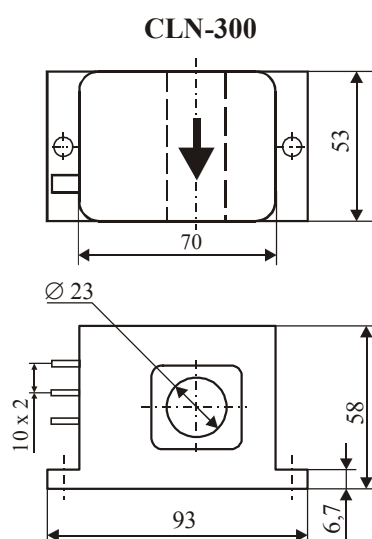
Внешний вид и габаритные размеры датчиков тока типа CLN-300, CLN-500
